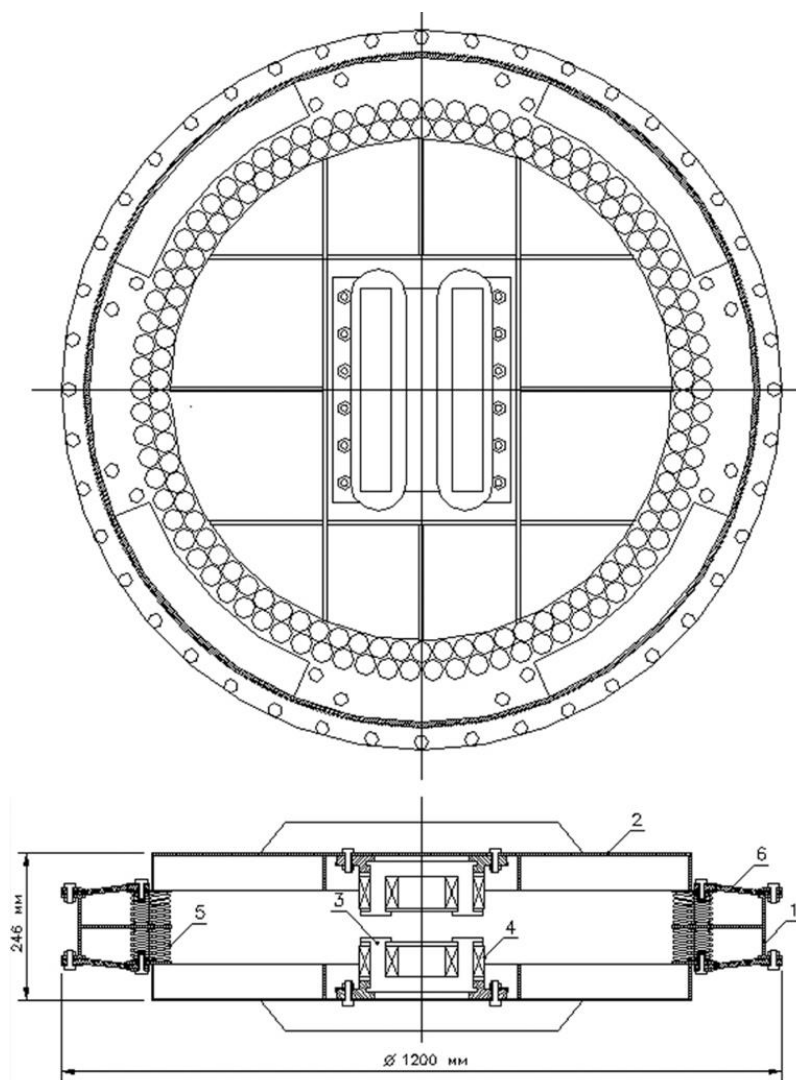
Схема конструкции гидроакустического излучателя 19–26 Гц
